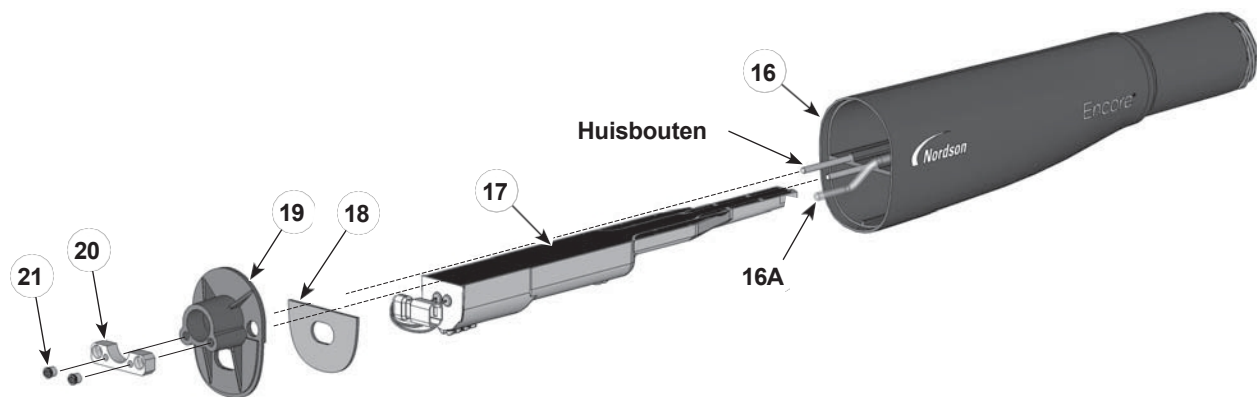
Pistool Demontage - Vervanging van kabelhouder en haakse fitting
